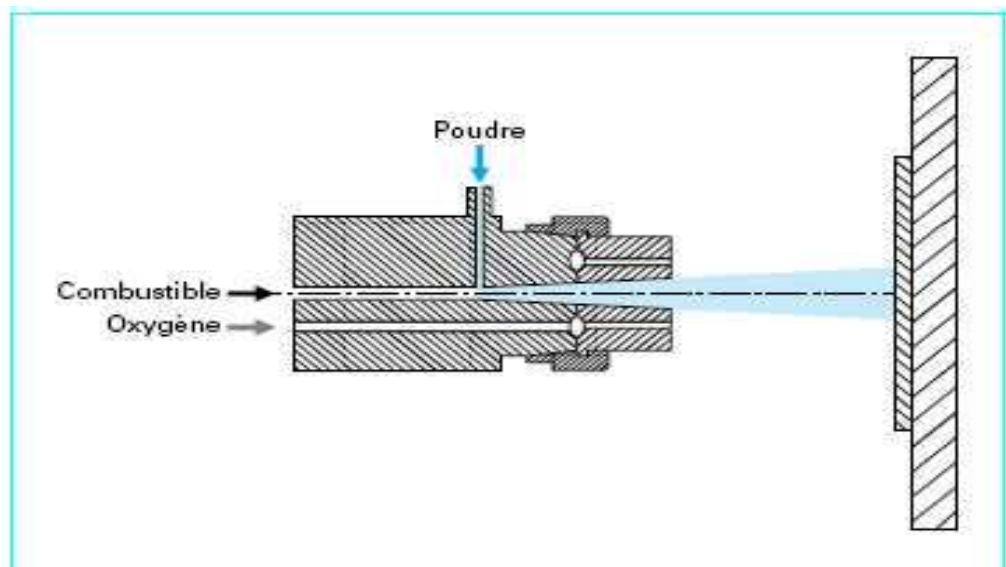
Schéma de principe d'un pistolet flamme-poudre [18].
